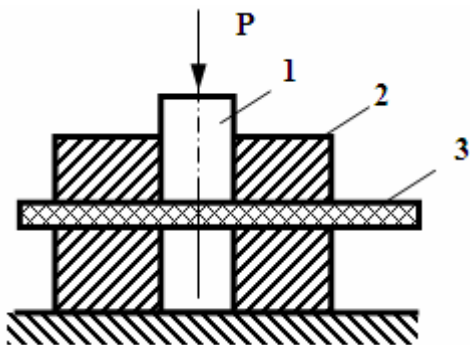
Схема испытаний при сдвиге (срезе): 1 – пуансон; 2 – обойма; 3 – испытываемый образец
